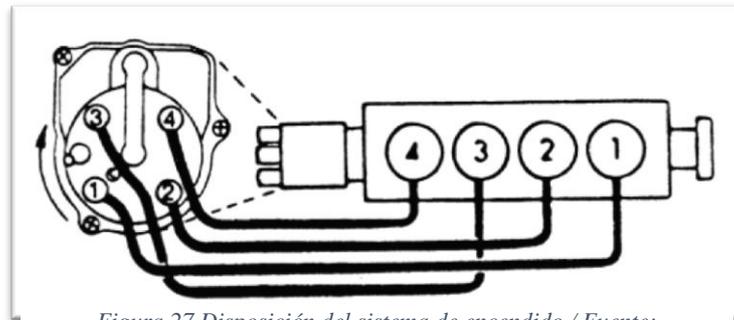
Disposición del sistema de encendido / Fuente: www.todomotores.cl
